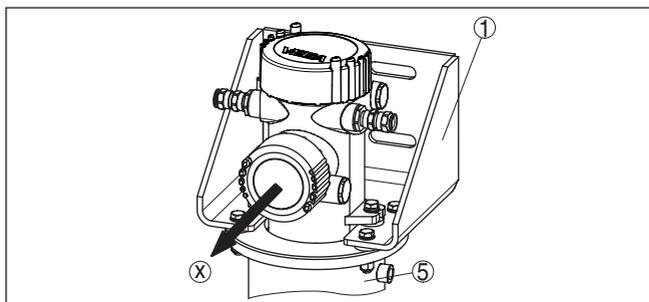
Direzione di montaggio del sensore rispetto alla squadretta di fissaggio
